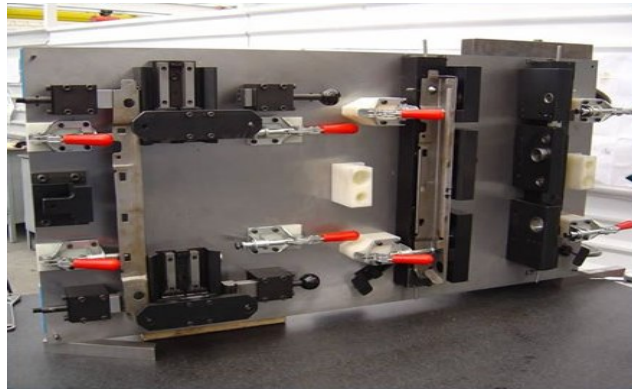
Vista superior de un Skid o pallet plano para ensamblaje automotriz
